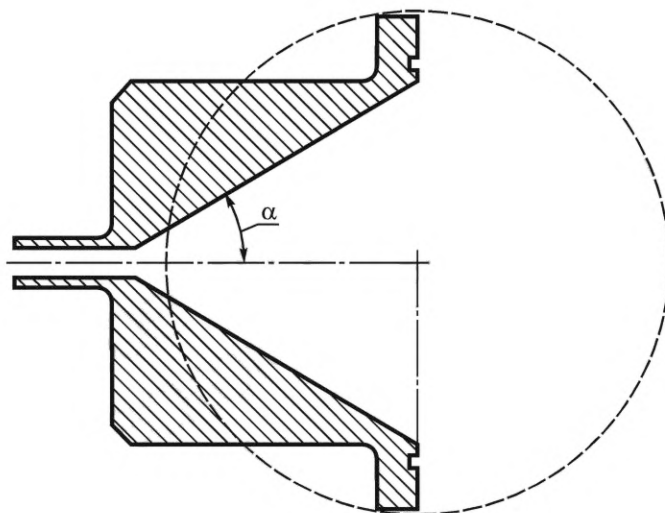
Эскиз фильтродержателя в разрезе, вид сбоку
